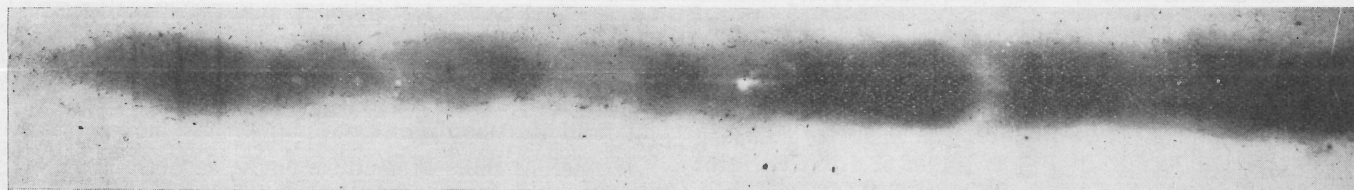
Radiographie d'une soudure en X (épaisseur 20 mm) : manque de pénétration avec inclusion de laitier.
